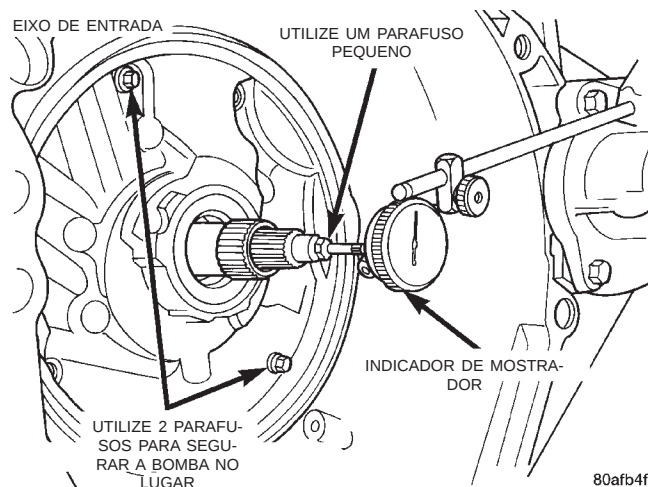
Medida do Jogo Axial do Eixo de Entrada
